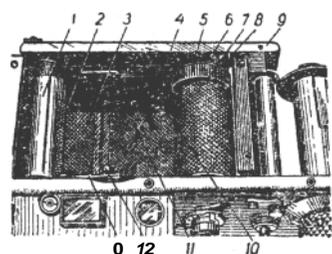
Шторный затвор в рабана. На противоположном корпусе. конце каждой шторки прикреплена металлическая планка (борка) 6. С обеих сторон борки прикреплены тесемки 7, концы которых приклеены к шкивам 9. Концы тесемок шторки барабана приклеены по обеим сторонам гильзы L
